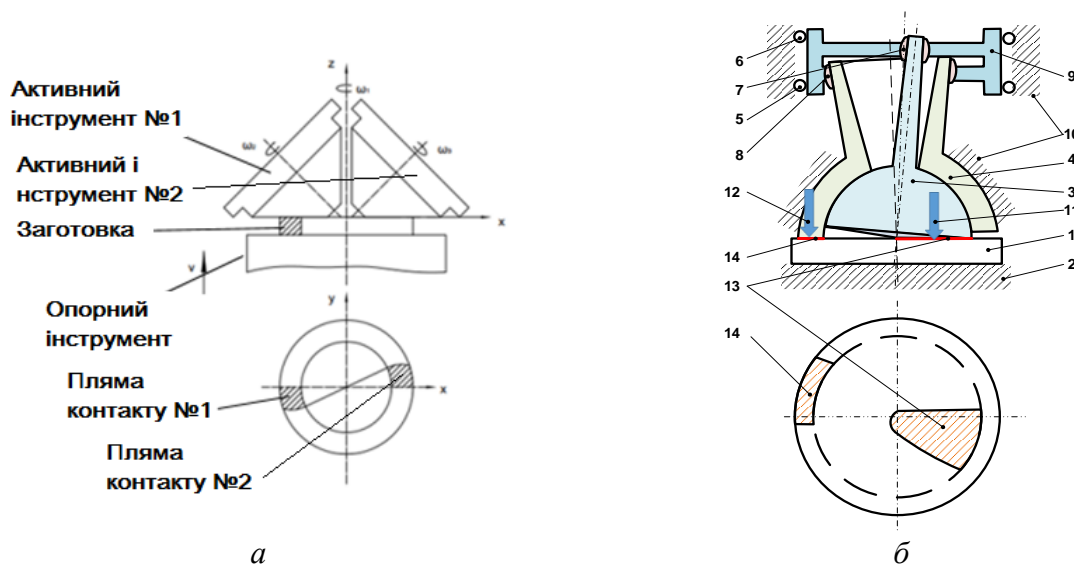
Механізми обкочування, які мають два приводних активних інструменти, що створюють врівноважені деформуючі зусилля (1 – заготовка; 2 – опорний інструмент; 3 – внутрішній активний інструмент; 4 – зовнішній активний інструмент; 5, 6 – підшипники; 7, 8 – сферичні підшипники; 9 – ротор; 10 – корпус; 11, 12 – деформуючі зусилля; 13, 14 – плями контакту):
